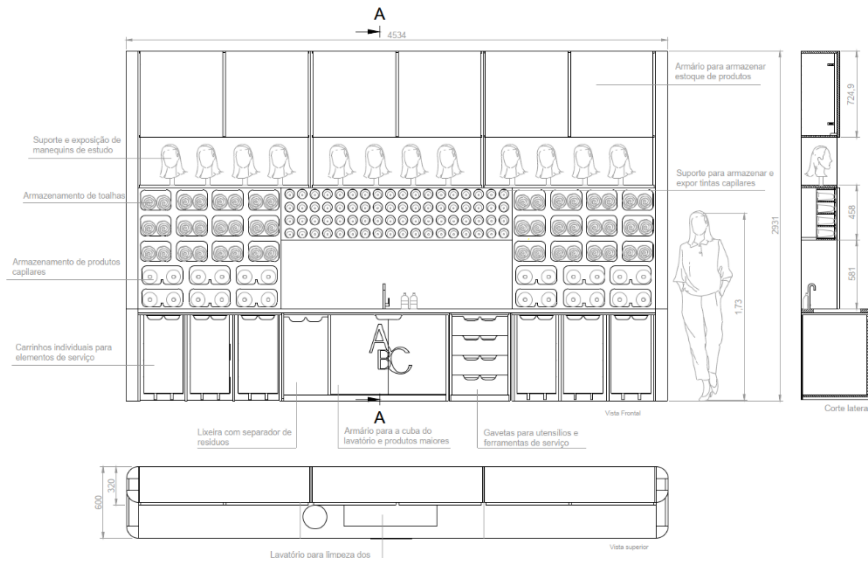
Vistas e corte do equipamento em utilização. Fonte: Autor.
